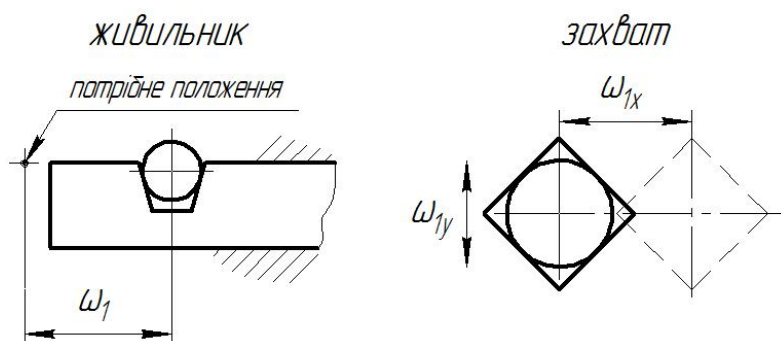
Похибка позиціонування рухомих вузлів завантажувального пристрою
